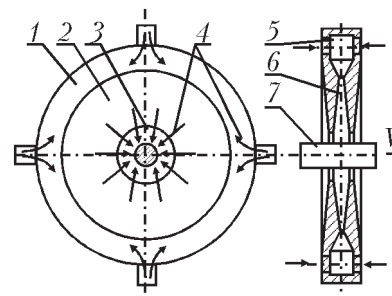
Схема дискового ускорителя для нанесения покрытий на внешнюю поверхность металлоконструкций. 1, 2 – корпус; 3, 7 – обрабатываемая металлоконструкция; 4 – направление движения гетерогенного потока; 5 – кольцевой коллектор (форкамера); 6 – дисковый ускоряющий канал
